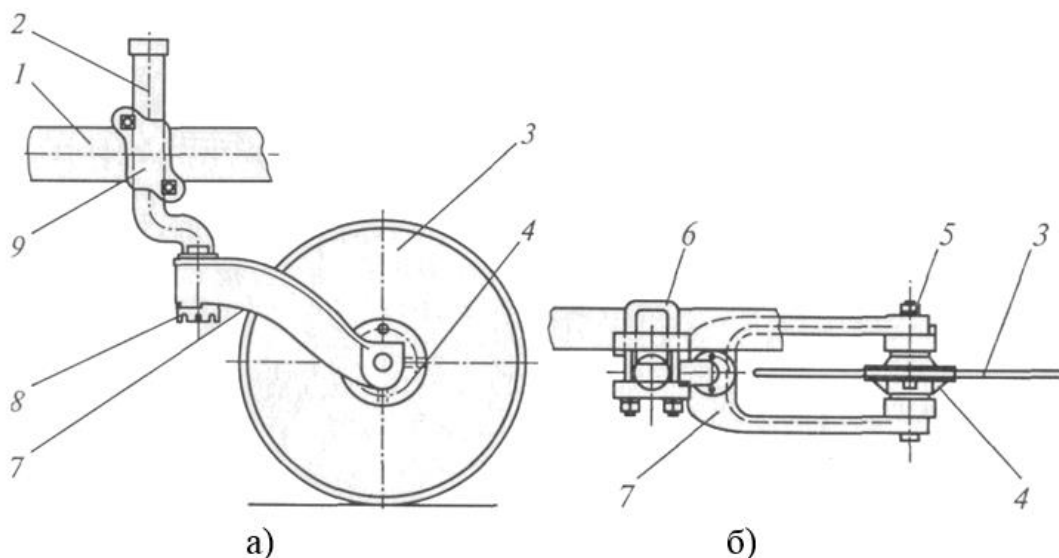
Дисковий ніж: а) – вид з боку; б) – вид зверху; 1 – рама плуга; 2 – стійка; 3 – диск; 4 – ступиця; 5 – вісь; 6 – скоба; 7 – вилка; 8 – корончата гайка; 9 – державка
